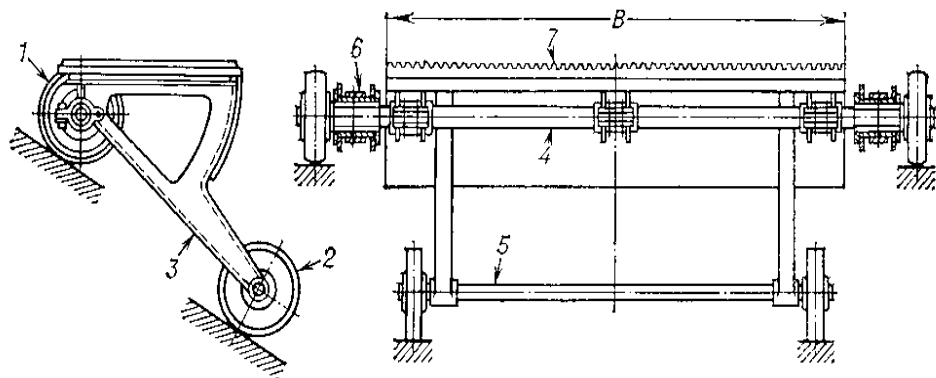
Схема ступени эскалатора: 1,2- ролики ,3-рама 4- полуось , 5-ось, 6-звездочки , 7-платформа
